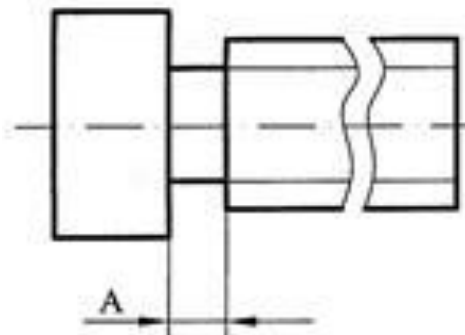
Схема заготовки с зарезьбовой зоной A
